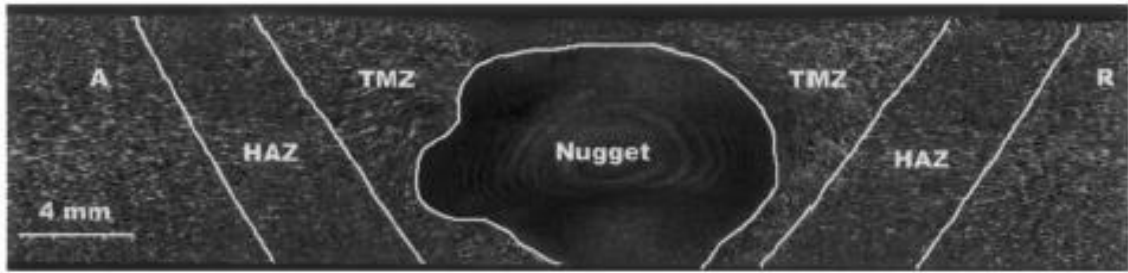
Macrostructure d'un joint soudé par FSW en alliage d'aluminium 2024-T351 - Coupe transversale (TL-TC) [38]
